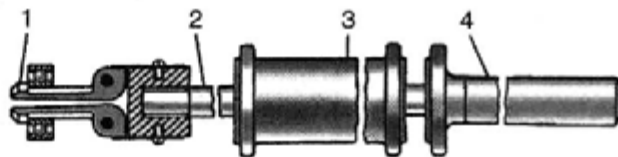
Съемник 7823-6090 для выпрессовки подшипника из коленчатого вала:
